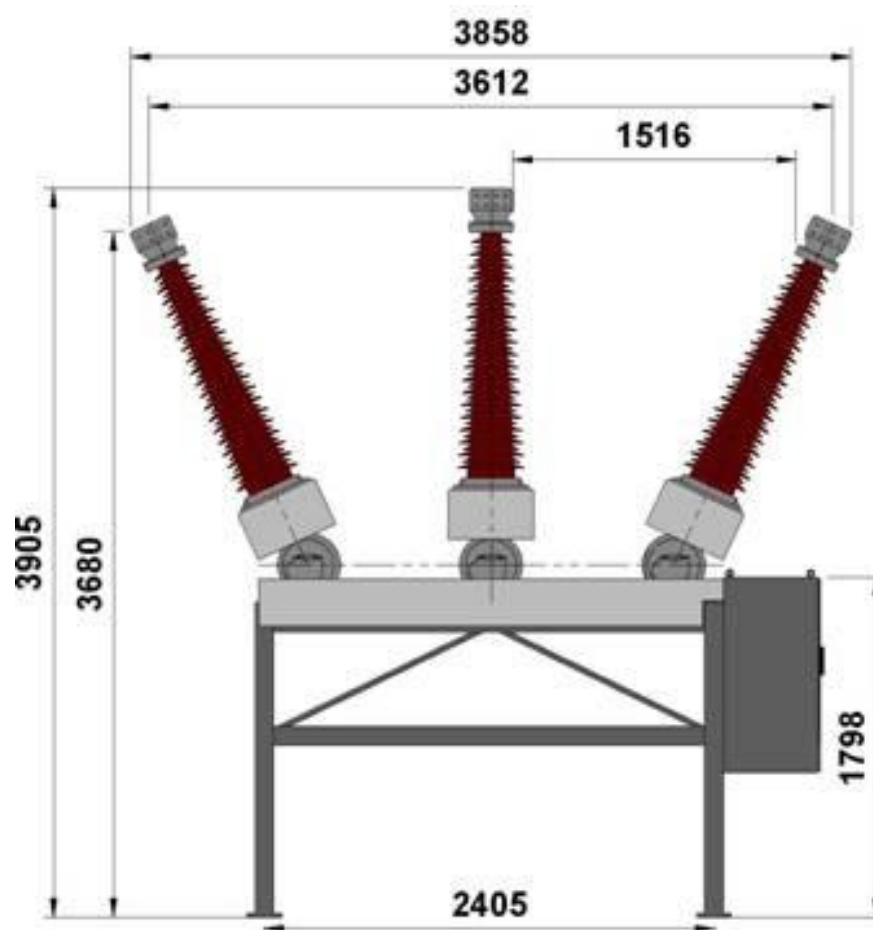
Габаритные размеры бакового выключателя ВГБ-110-31,5/1000 У1
